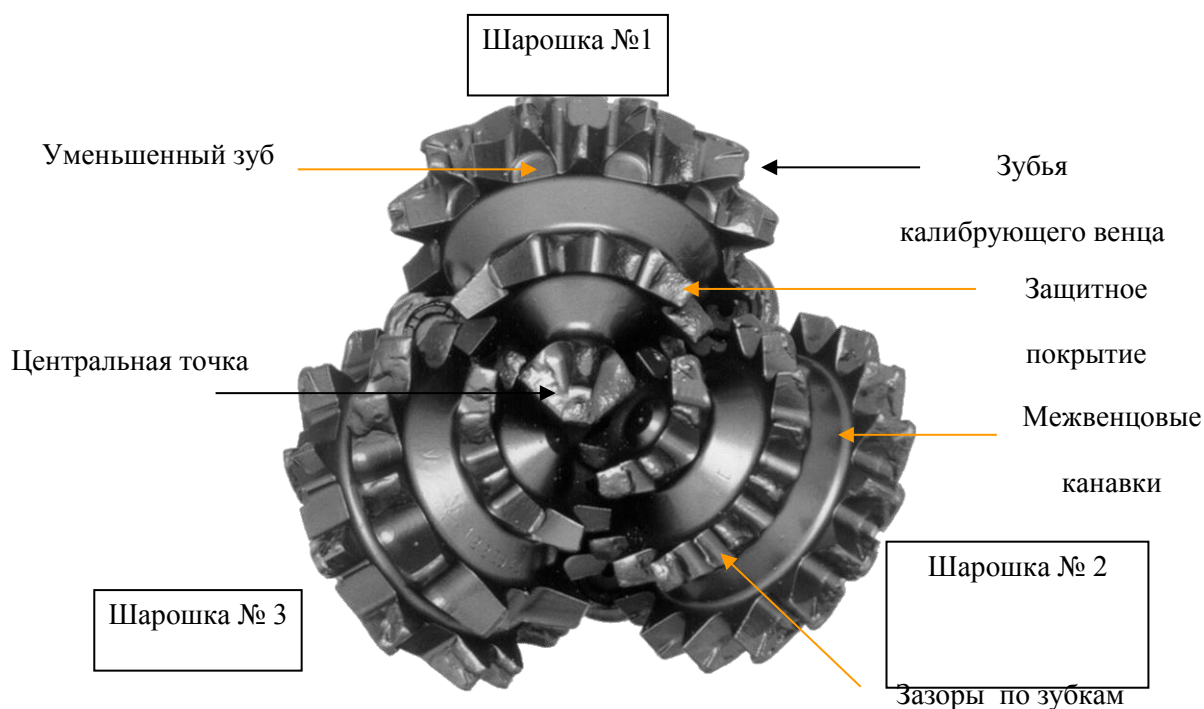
Номенклатура деталей долота с фрезерованными зубьями
